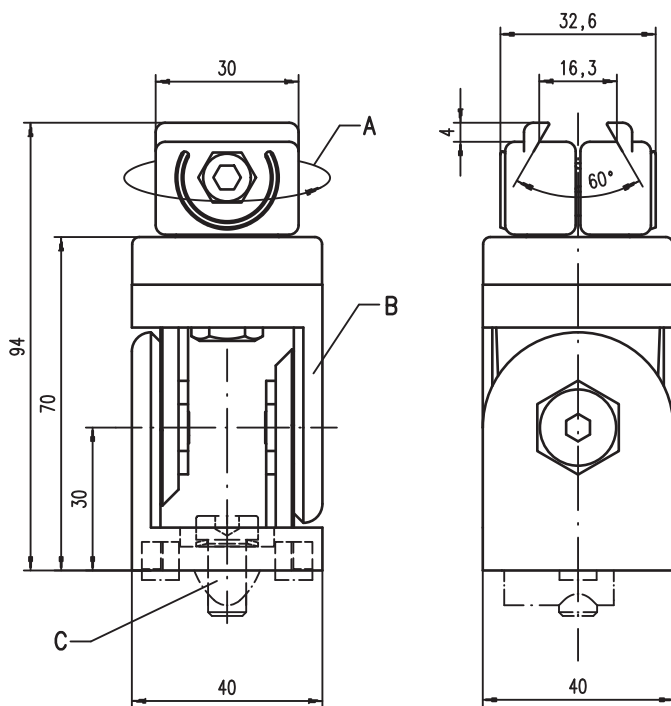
Maßzeichnung Schwenkspiegelscanner
